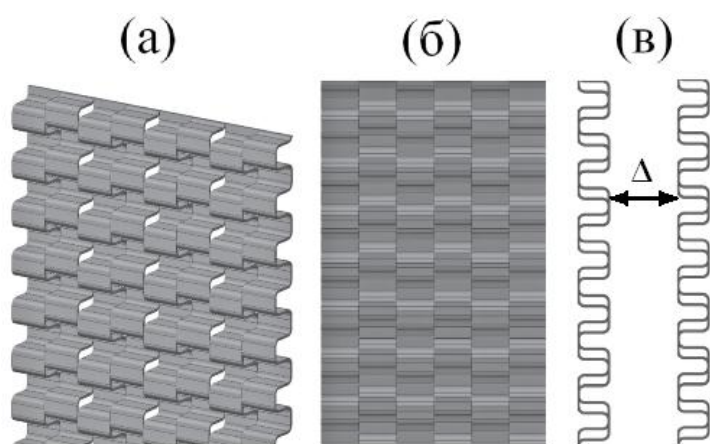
Элемент ГПН-насадки в изометрии (а); вид на элемент насадки спереди (б); вид сбоку на блок насадки (в)
